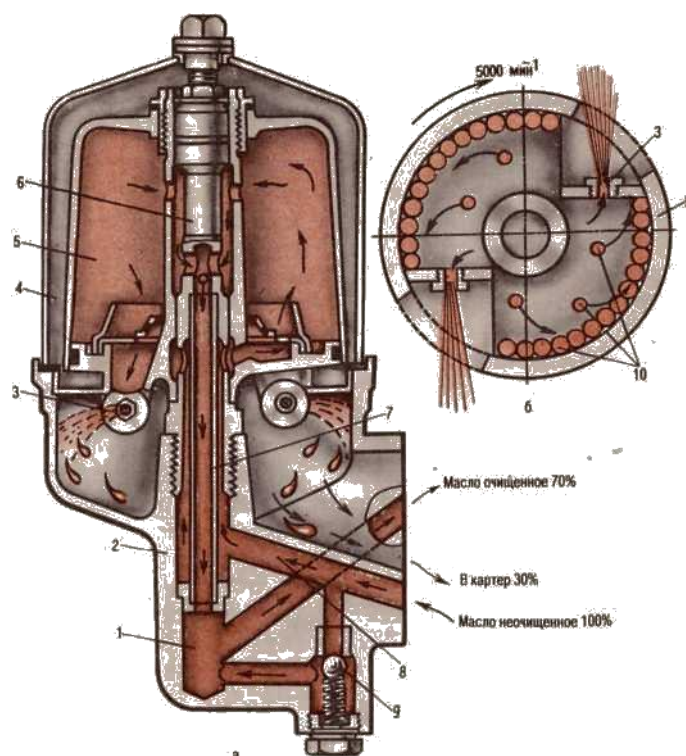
Полнопоточный центробежный маслоочиститель:
